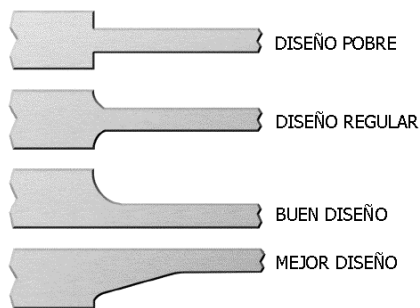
Formas recomendadas de cambio de sección. Fuente: Hitchiner Manufacturing Co. Inc., *Designing for investment casting, Technical Updated 2D1*.
